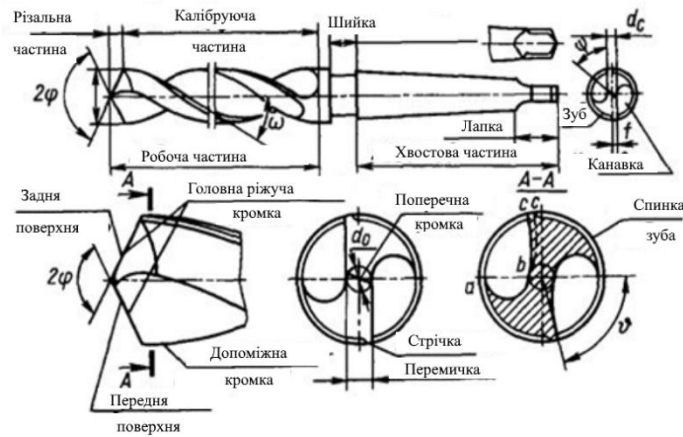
Конструктивні елементи спірального свердла [4].
